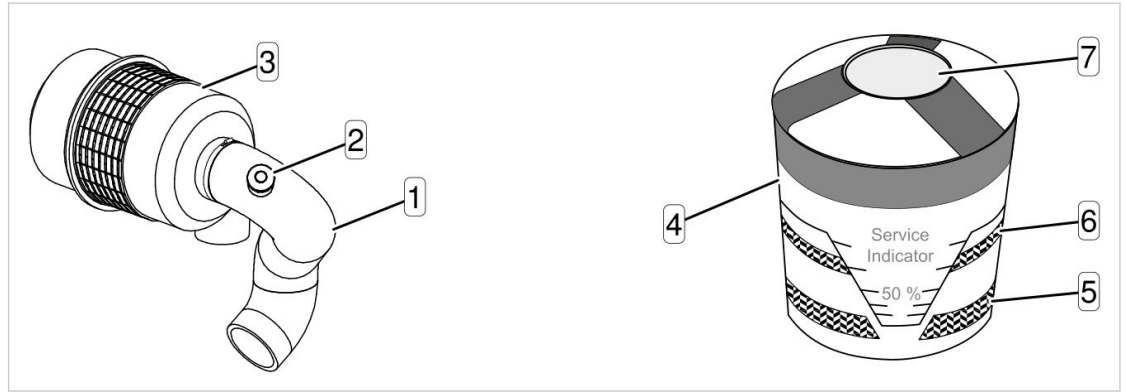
Controlar el indicador de mantenimiento del tubo de aspiración del filtro de aire del compresor
